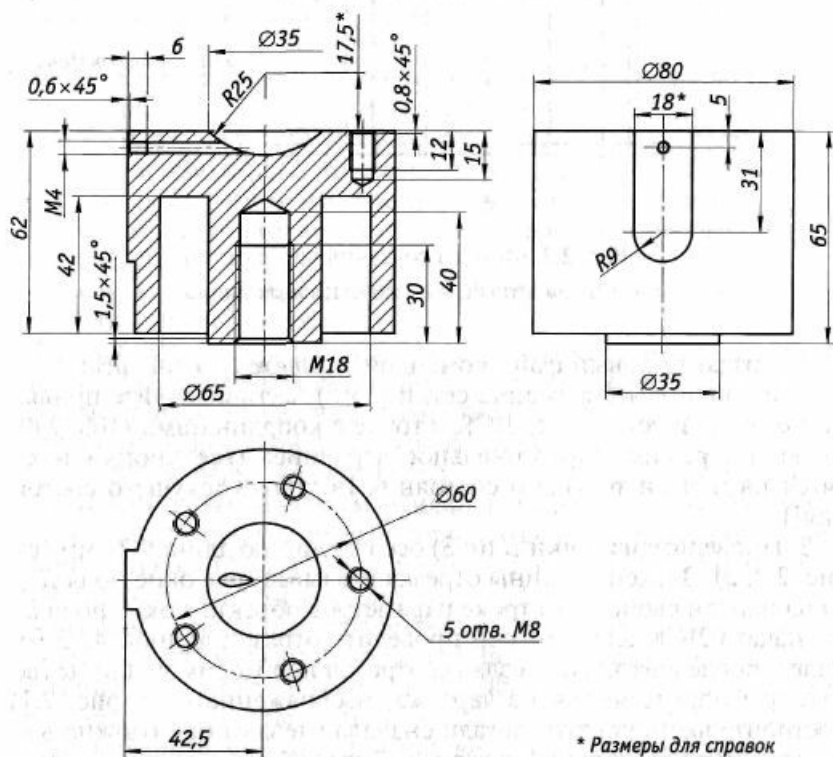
Фрагмент чертежа направляющего цилиндра
